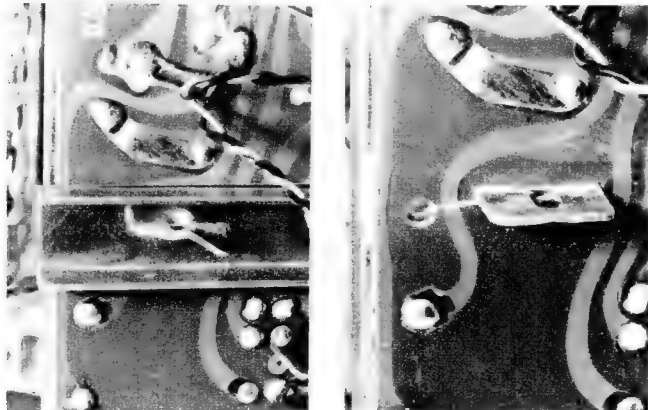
Printplatte mit dem Befestigungsblech für den Transformator
